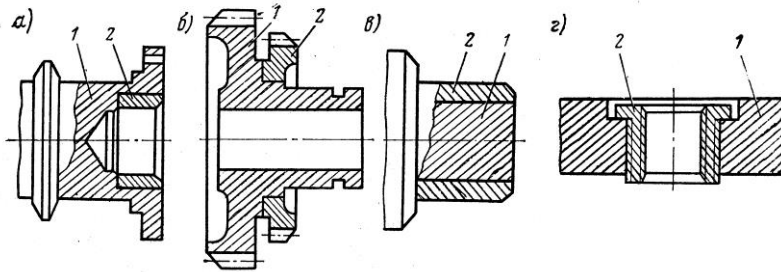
Відновлення зношених деталей встановленням додаткових деталей: а – внутрішніх поверхонь отворів; б – шестерень; в – шийок цапф; г – різьбі; 1 – зношена деталь; 2 – додаткова деталь
